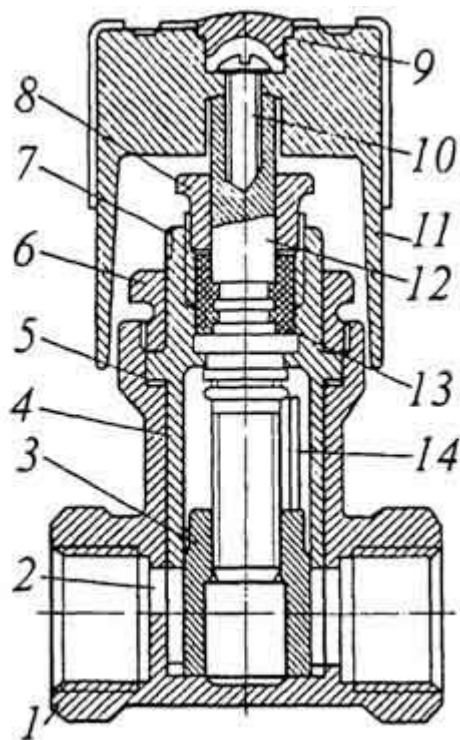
Кран двойной регулировки шиберный типа КРДШ: 1 - корпус; 2 - регулировочное окно; 3 - шибер; 4 - поворотная втулка; 5 - прокладка; 6 - закрепительная гайка; 7 - установочная риска на втулке; 8 - гайка сальника; 9 - крышка; 10 - винт; 11 - ручка; 12 - резьбовой шпиндель; 13 - сальниковое уплотнение; 14 - паз во втулке
